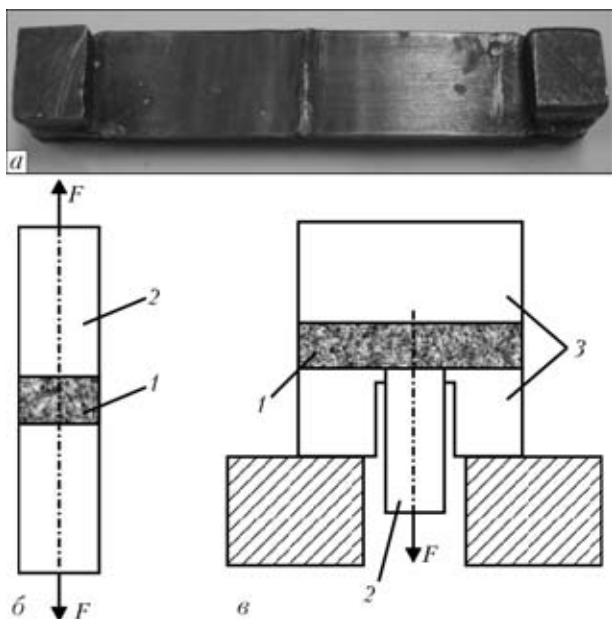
Образец основного типа (а) и схемы испытания на замедленное разрушение его (б) и специального образца (в) стыкового соединения: 1 — шов; 2 — рабочая (испытываемая) часть; 3 — вспомогательные части
